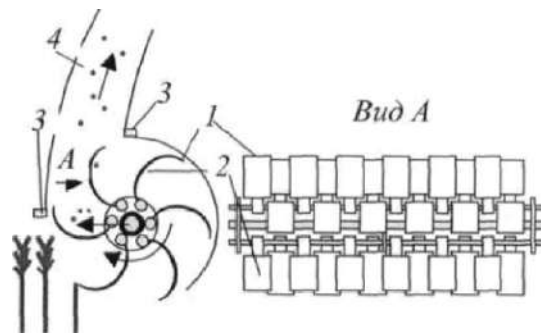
Роторний подрібнювальний апарат із шарнірно закріпленими ножами: 1 – лезо ножа; 2 – кидальна лопатка ножа; 3 – протирізальна пластина; 4 – вивантажувальний патрубок
